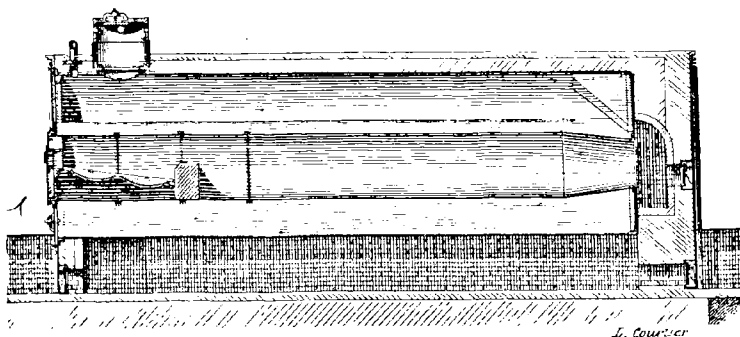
Chaudière de Lancastre (coupe longitudinale).
